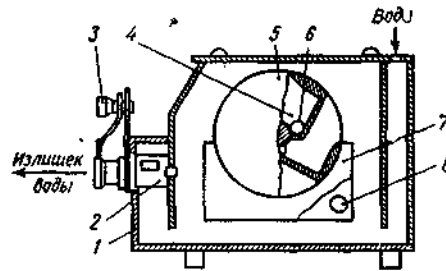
Схема черпакового дозатора води преса ЛПЛ-2М
